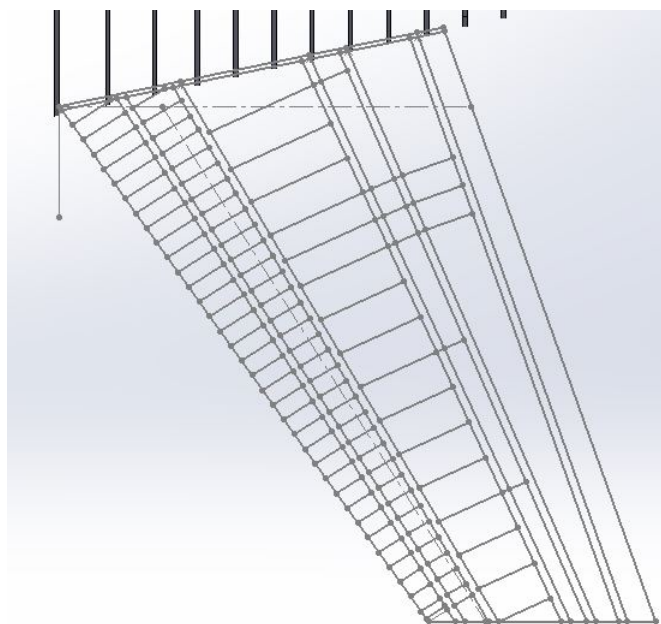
Vista en planta de l'estructura de l'estabilitzador horitzontal.
